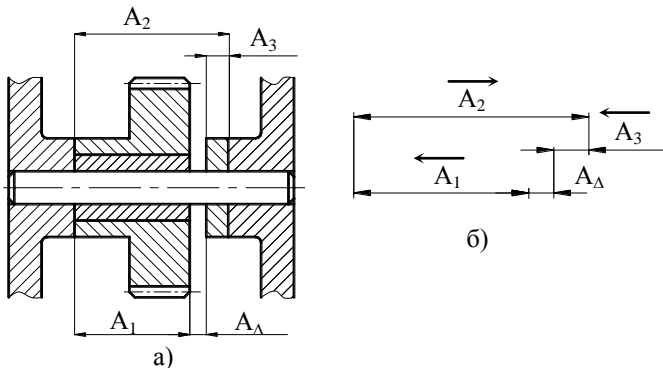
Лінійний розмірний ланцюг зубчастого колеса та проміжного кільця механізму: а) – загальний вигляд; б) – схема
